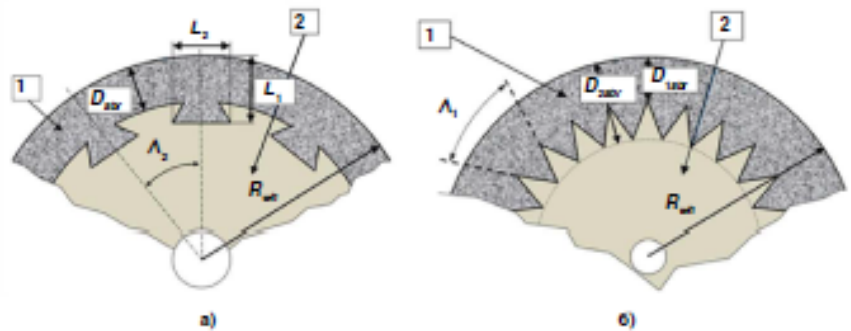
Общие схемы алмазных кругов для высокоскоростного шлифования разных конструкций: а) зубчатая; б) замковая: 1 — алмазоносный слой; 2 — корпус круга
